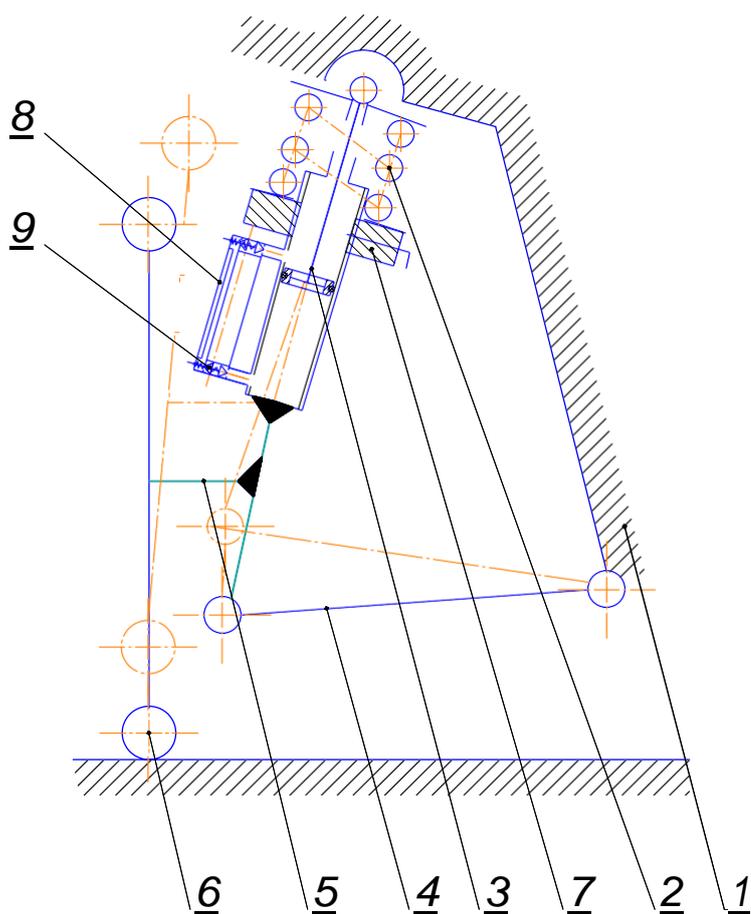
Кинематическая схема разрабатываемой подвески:
